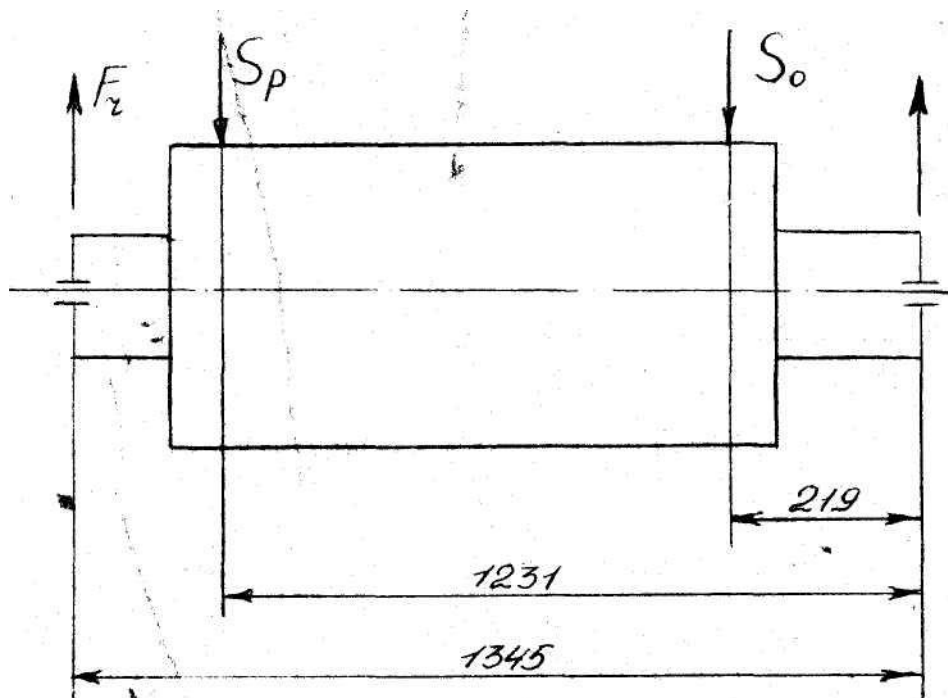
Схема для розрахунку підшипників у зубчастій напівмуфті редуктора
